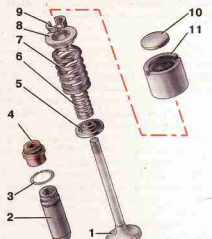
Детали механизма привода клапанов: 1 – клапан; 2 – направляющая втулка; 3 – стопорная колодка; 4 – маслоотражающий колпачок; 5 – опорная шайба пружин; 6 – внутренняя пружина; 7 – наружная пружина; 8 – тарелка пружин; 9 – сухарь; 10 – регулировочная шайба; 11 – толкатель
